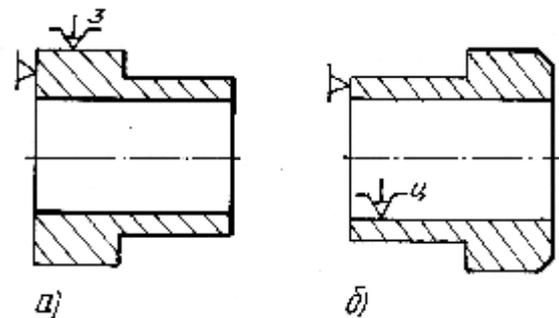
Условное обозначение закрепления заготовки при обработке на токарном станке: а – в патроне; б – на цанговой оправке
